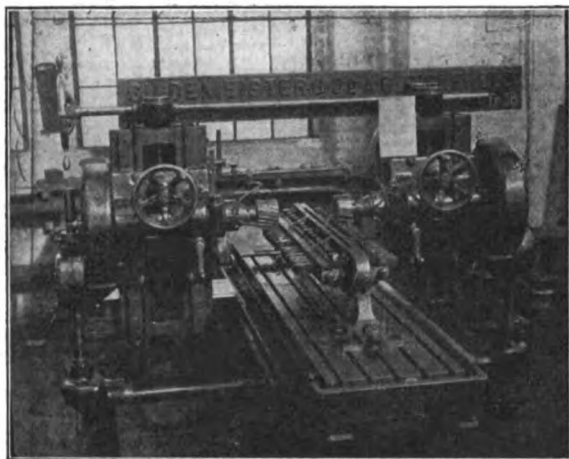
Fräsen der geraden und schrägen Flächen der Keilschrauben.
